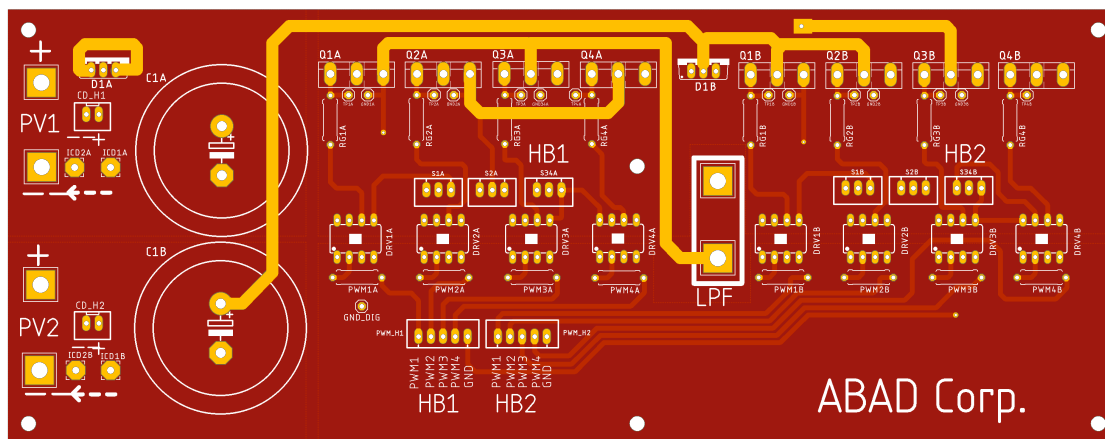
Vista previa del PCB en la capa superior antes de fabricar.
